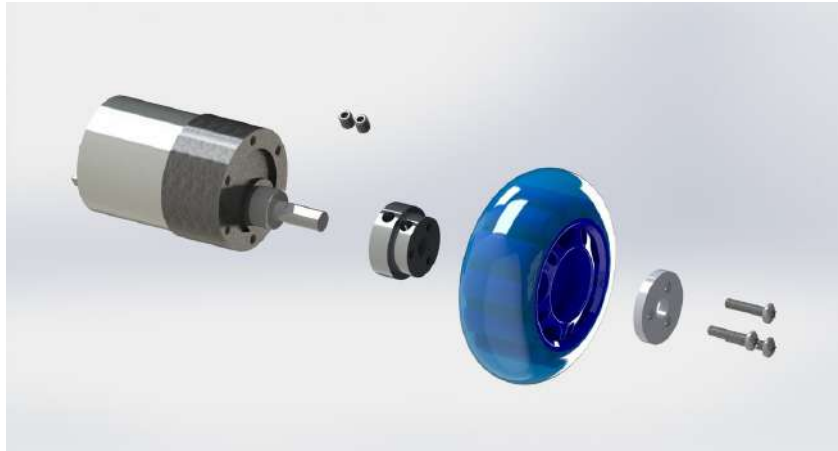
Vista explodida da montagem do adaptador de fixação. (POLULU (2017))
